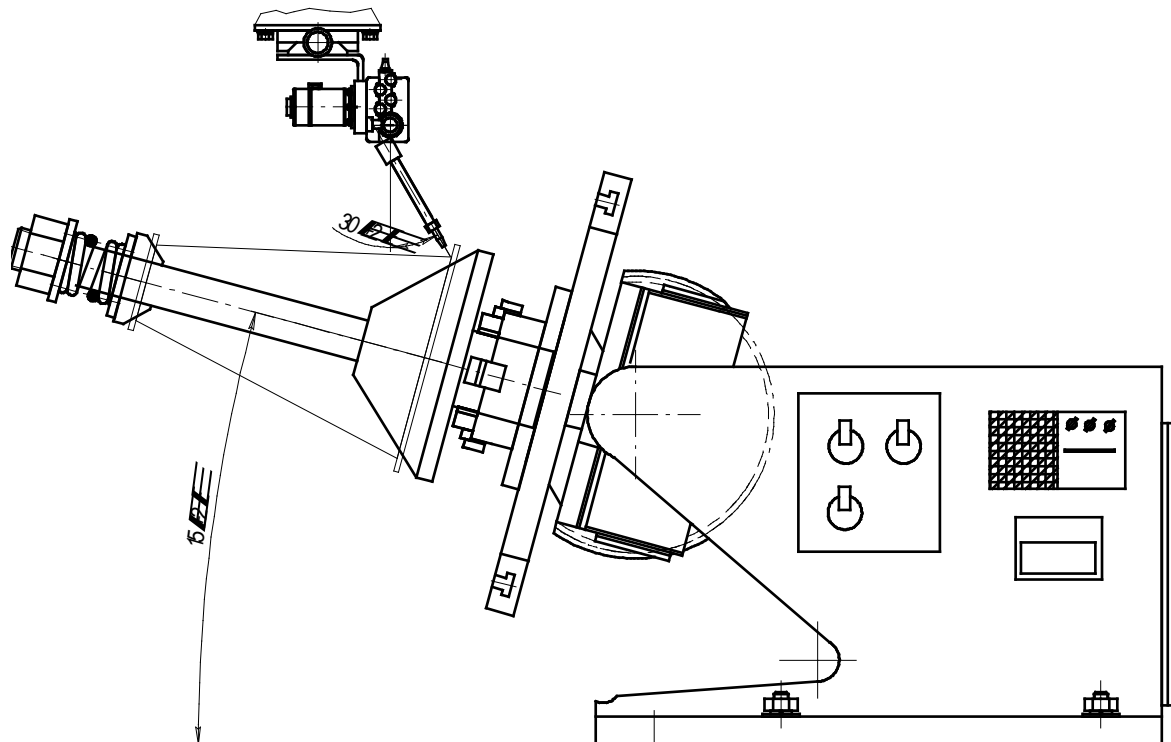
Схема настройки оборудования для сварки
